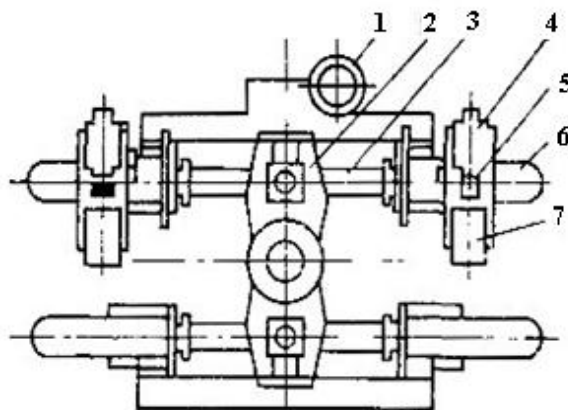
Схема компоновки четырехцилиндровой рулевой машины Р15:
